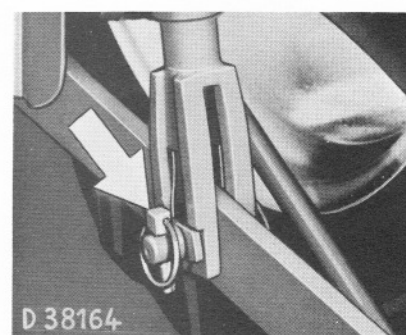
Fixation des chevilles à anneau après démontage de la barre d'attelage
